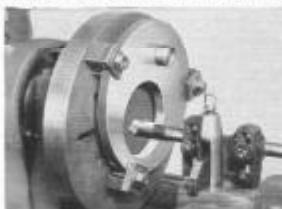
Hechura de un agujero excentrico sobre el plato del torno
